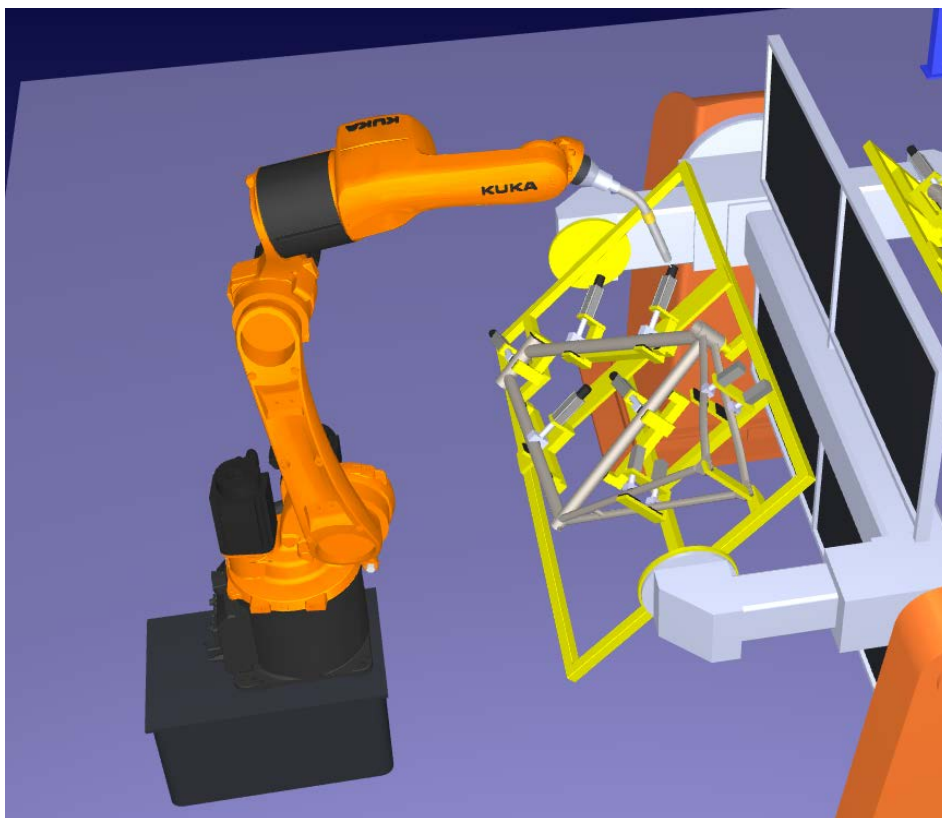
Загальний вигляд робота KUKA KR 16 R1610 з пальником FRONIUS для зварювання рами
